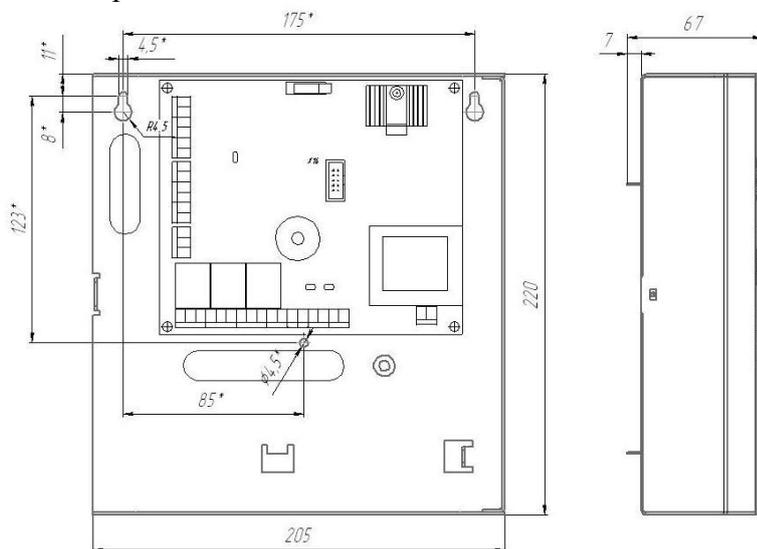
Габаритный чертеж и установочные размеры АПКП.
